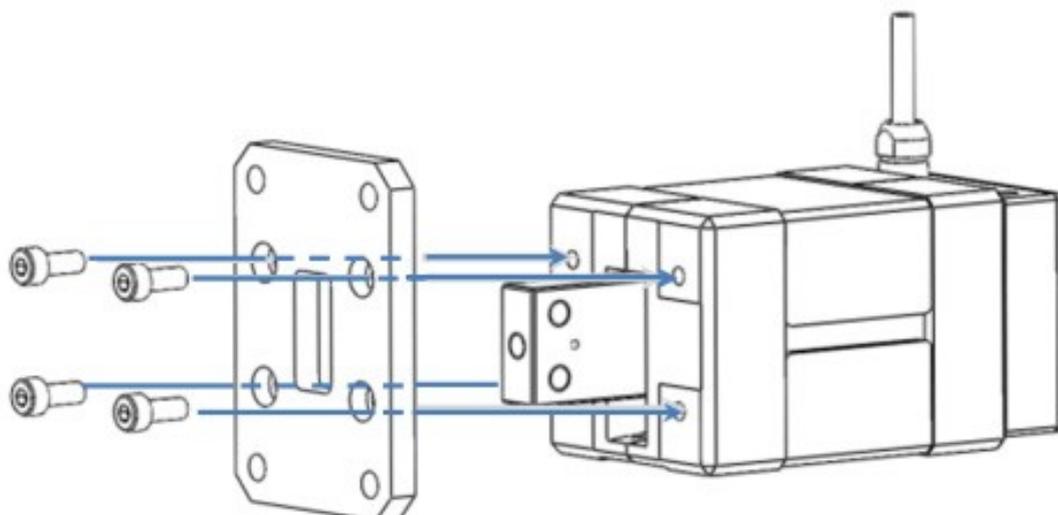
Montage des Montageflanschs B (Explosionsdarstellung)
